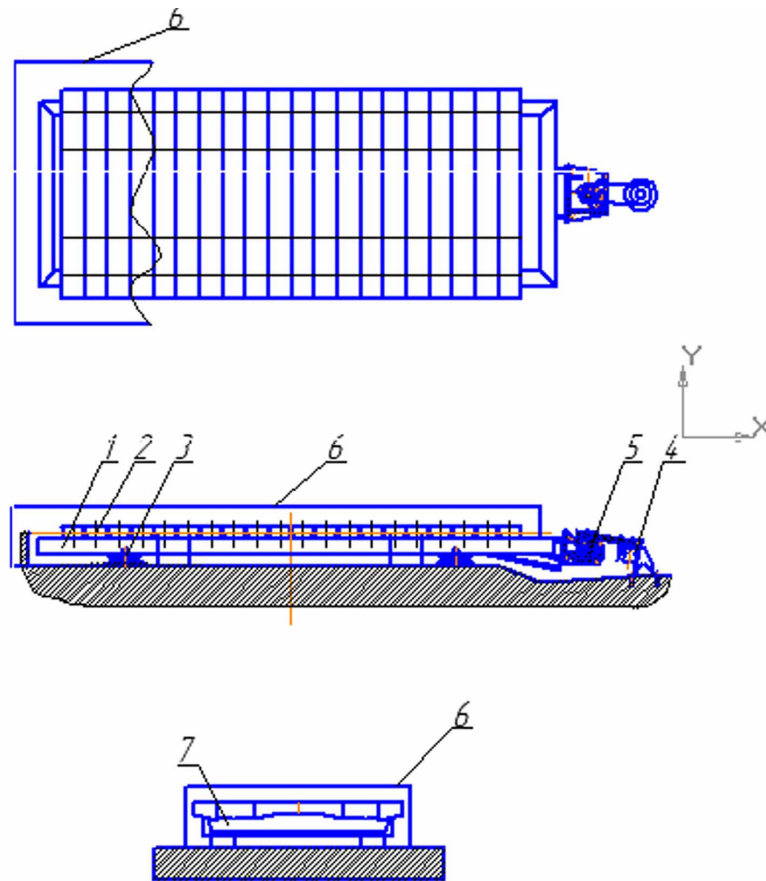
Принципова схема пристрою для виготовлення залізобетонних шпал.
